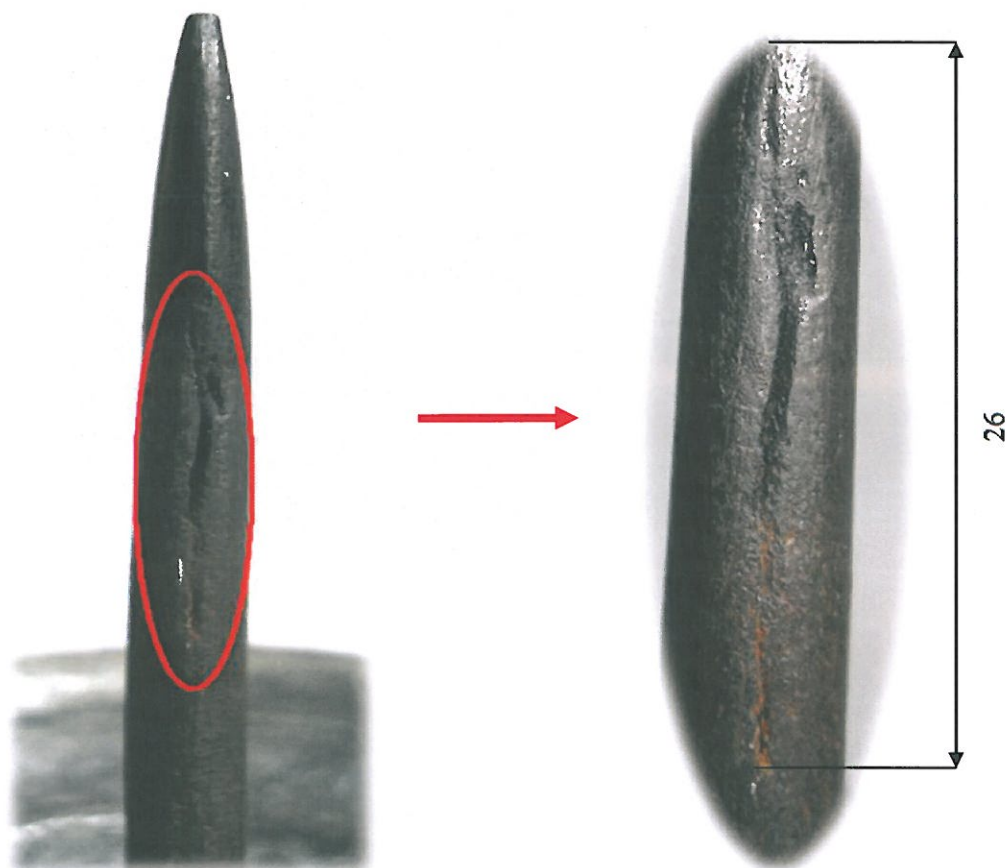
Praskliny jsou téměř po celé délce hřbetu nohy (v místě spoje)
